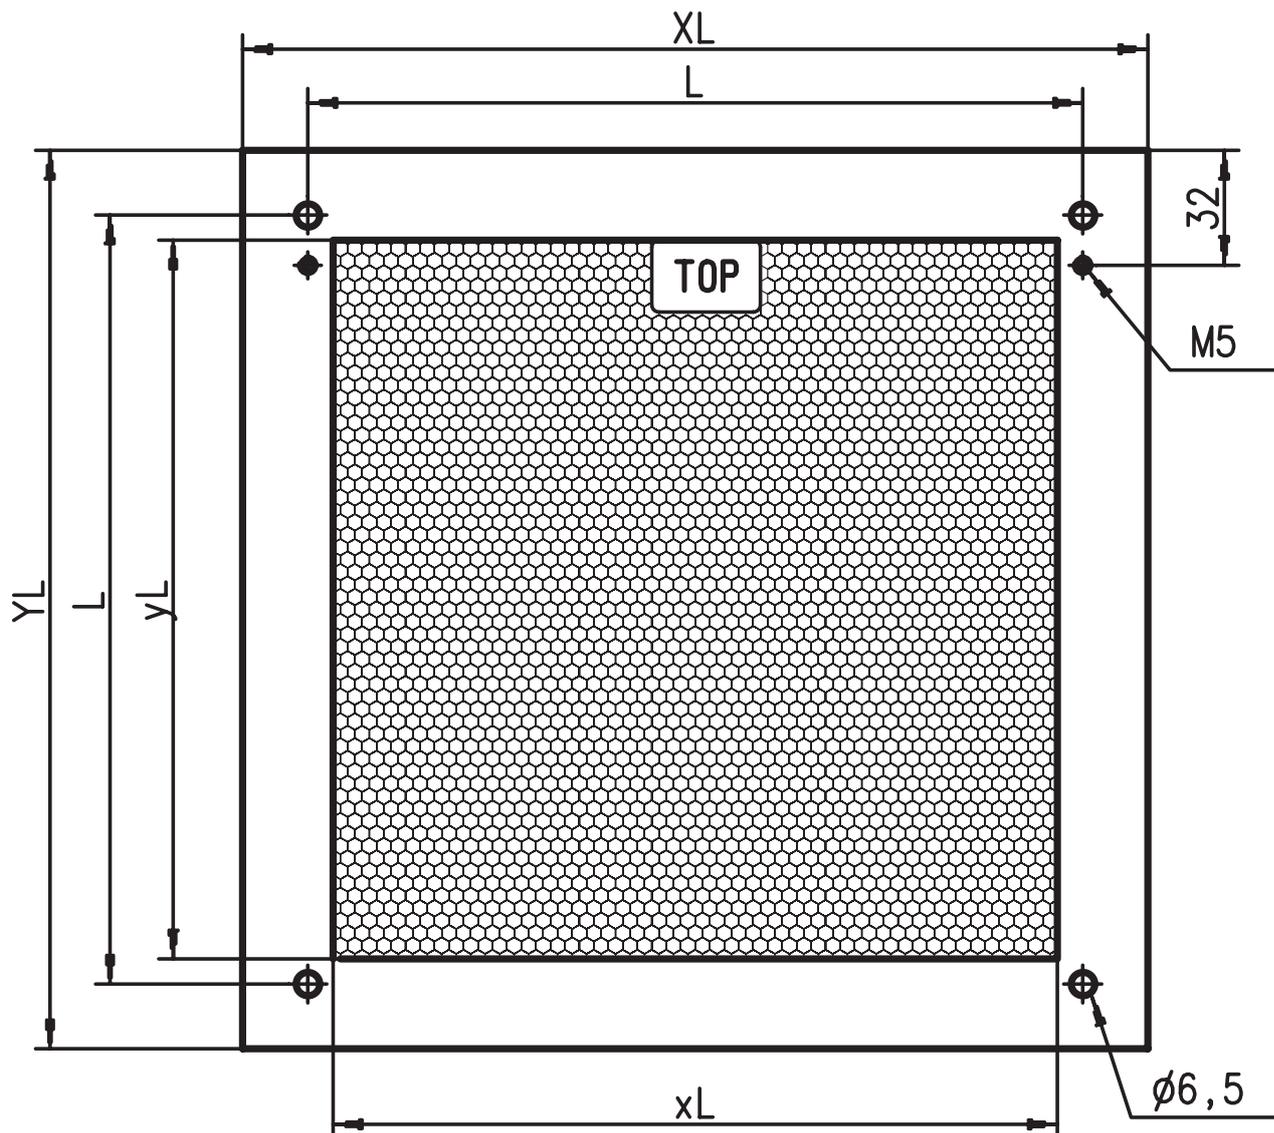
Encombrement de l'adhésif réfléchissant sur plaque de support
